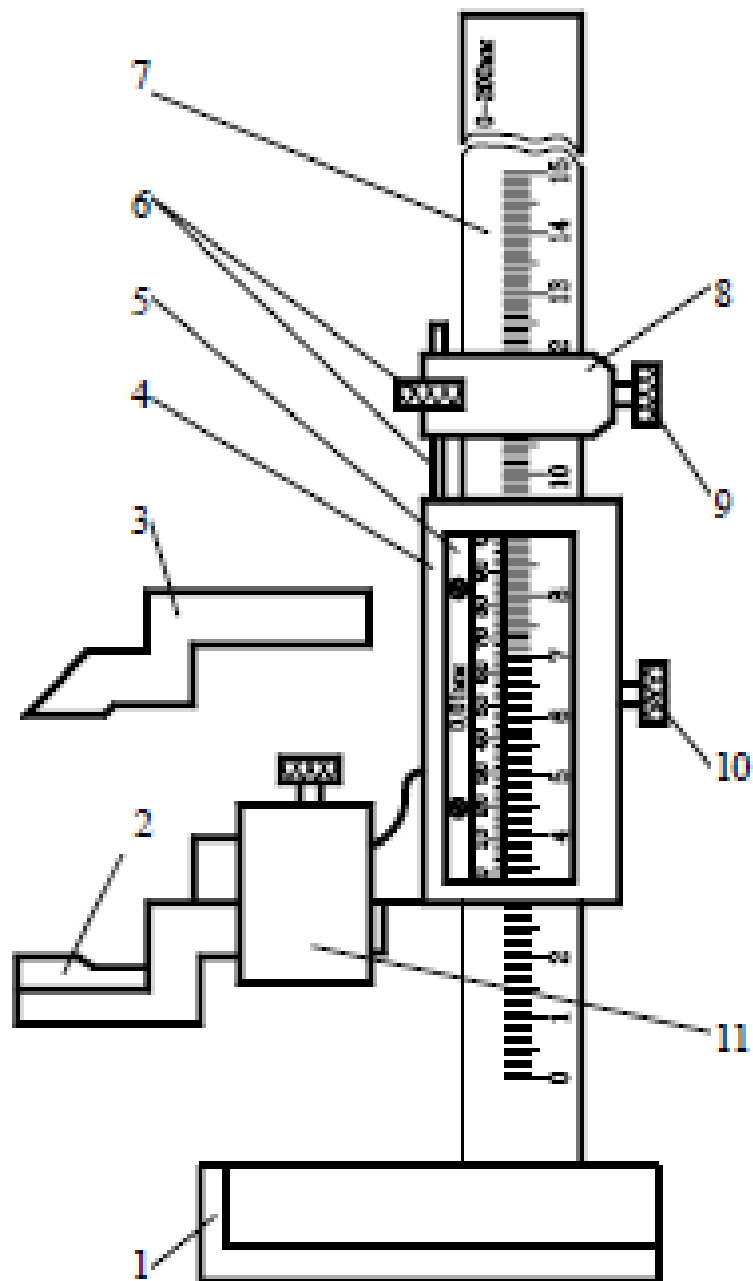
Штангенрейсмас: 1 – основание; 2 – измерительная ножка; 3 – разметочная ножка; 4 – рамка; 5 – нониус; 6 – винт и гайка микрометрической подачи; 7 – штанга; 8 – рамка микрометрической подачи; 9 – зажим рамки микрометрической подачи; 10 – зажим рамки; 11 – шпигун
